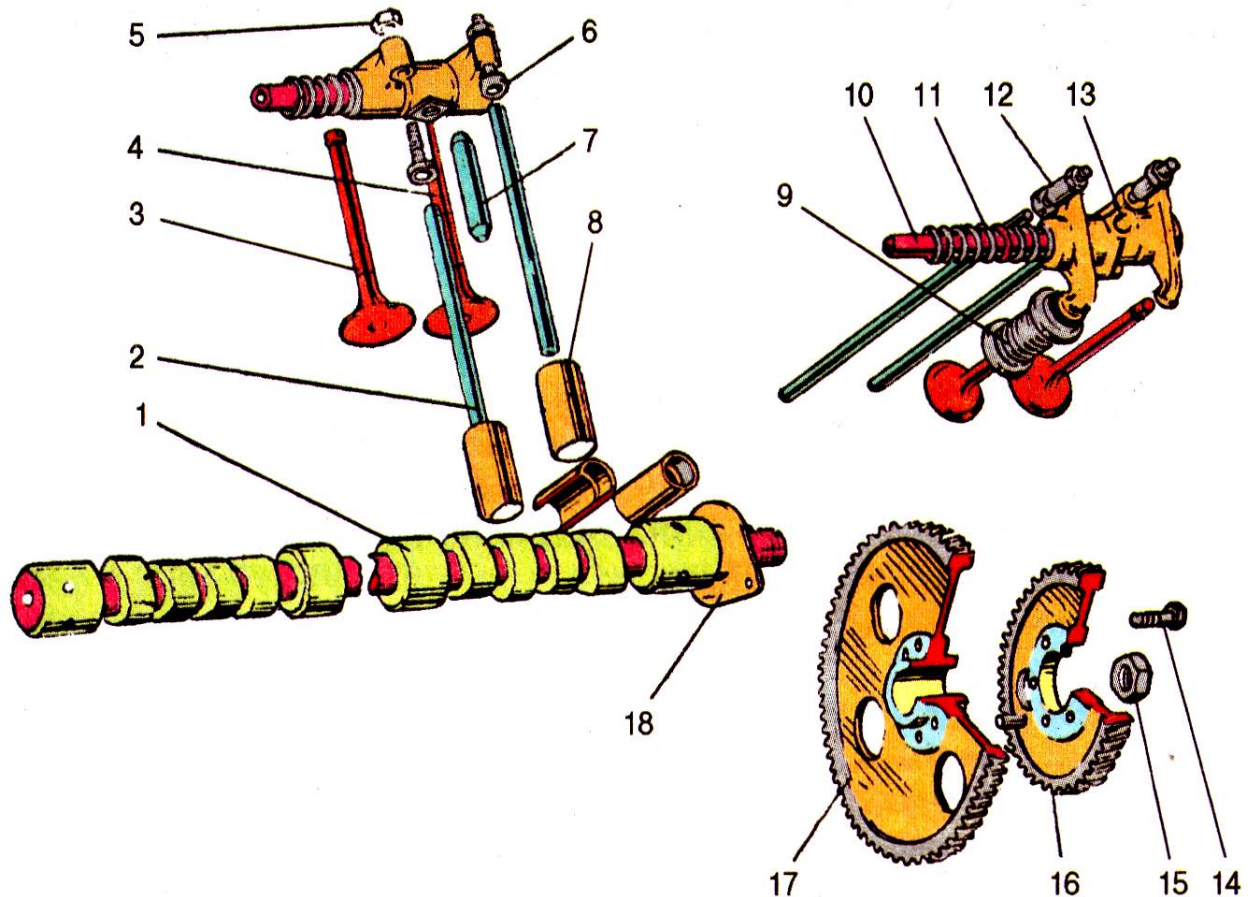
Газорозподільний механізм дизеля СМД-60:
